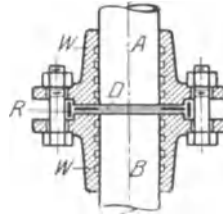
Flanschenverbindung mit Dichtungsschutzring.
